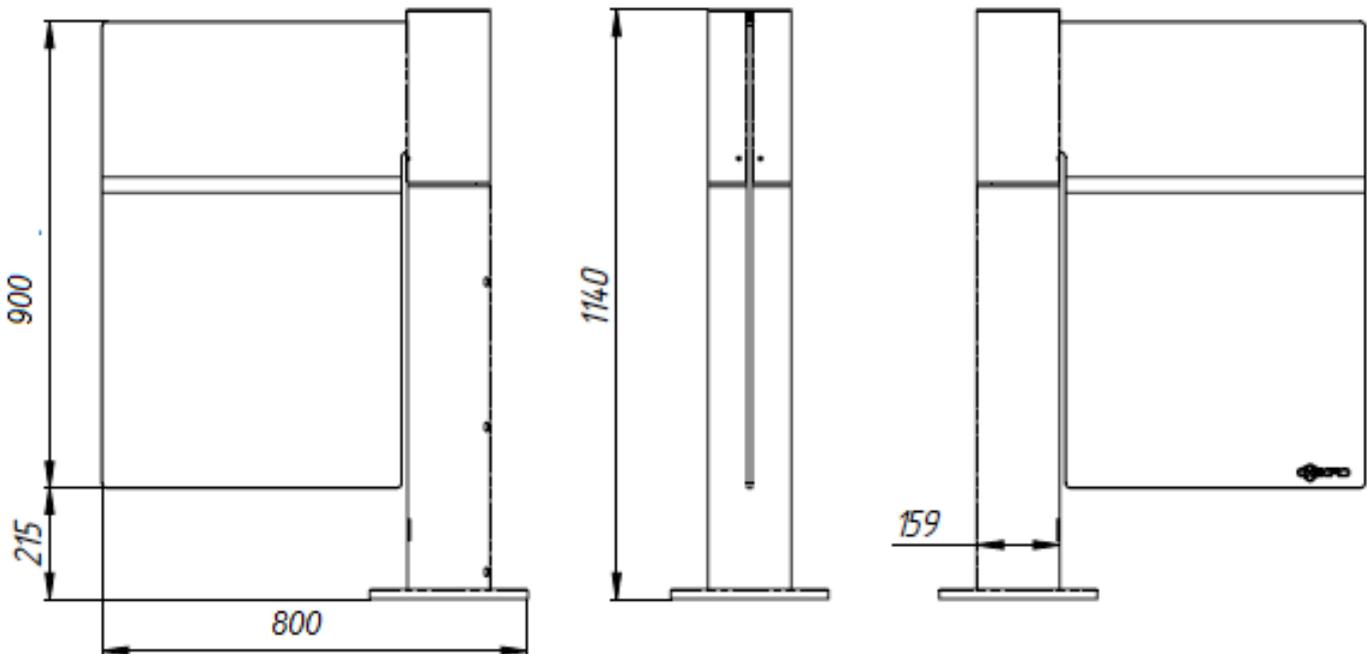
Габаритные размеры калитки шириной прохода 600 мм
